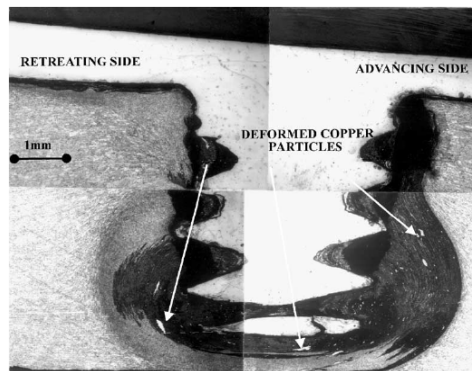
Corte de uma soldadura parada através da técnica de *stop-action* [8]
